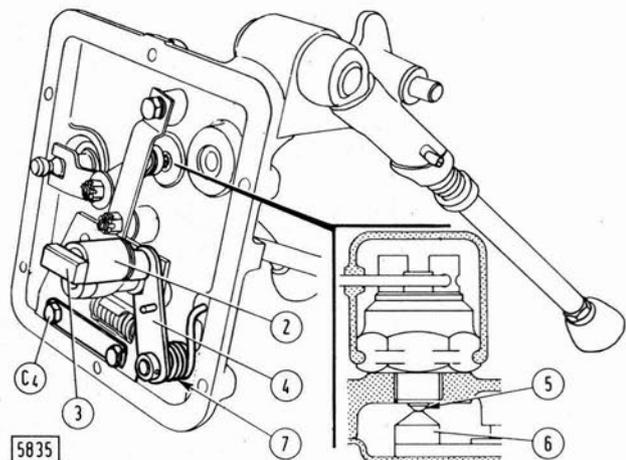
Couvercle du carter de boîte de vitesses avec dispositif de sélection.
